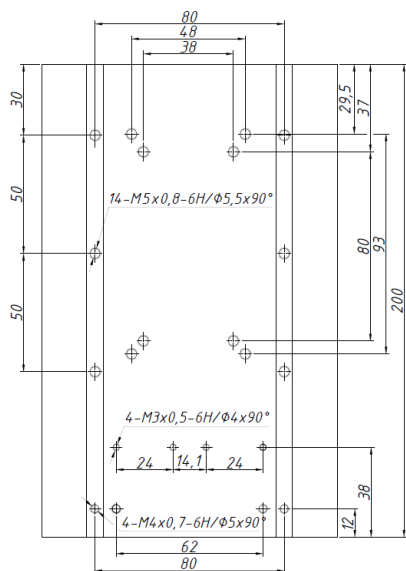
габаритные и установочные размеры радиатора PTR039
